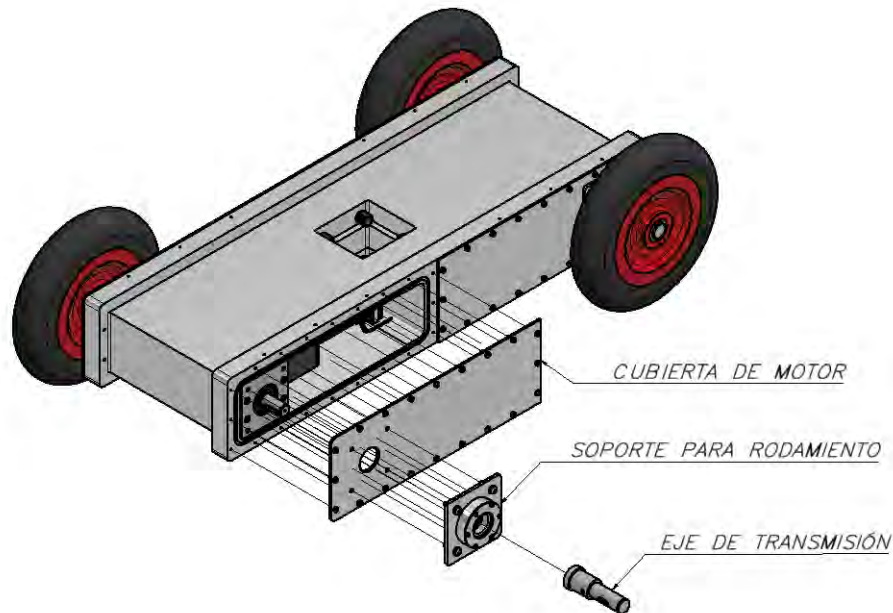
Ensamble del aprisionamiento del motor-reductor.
